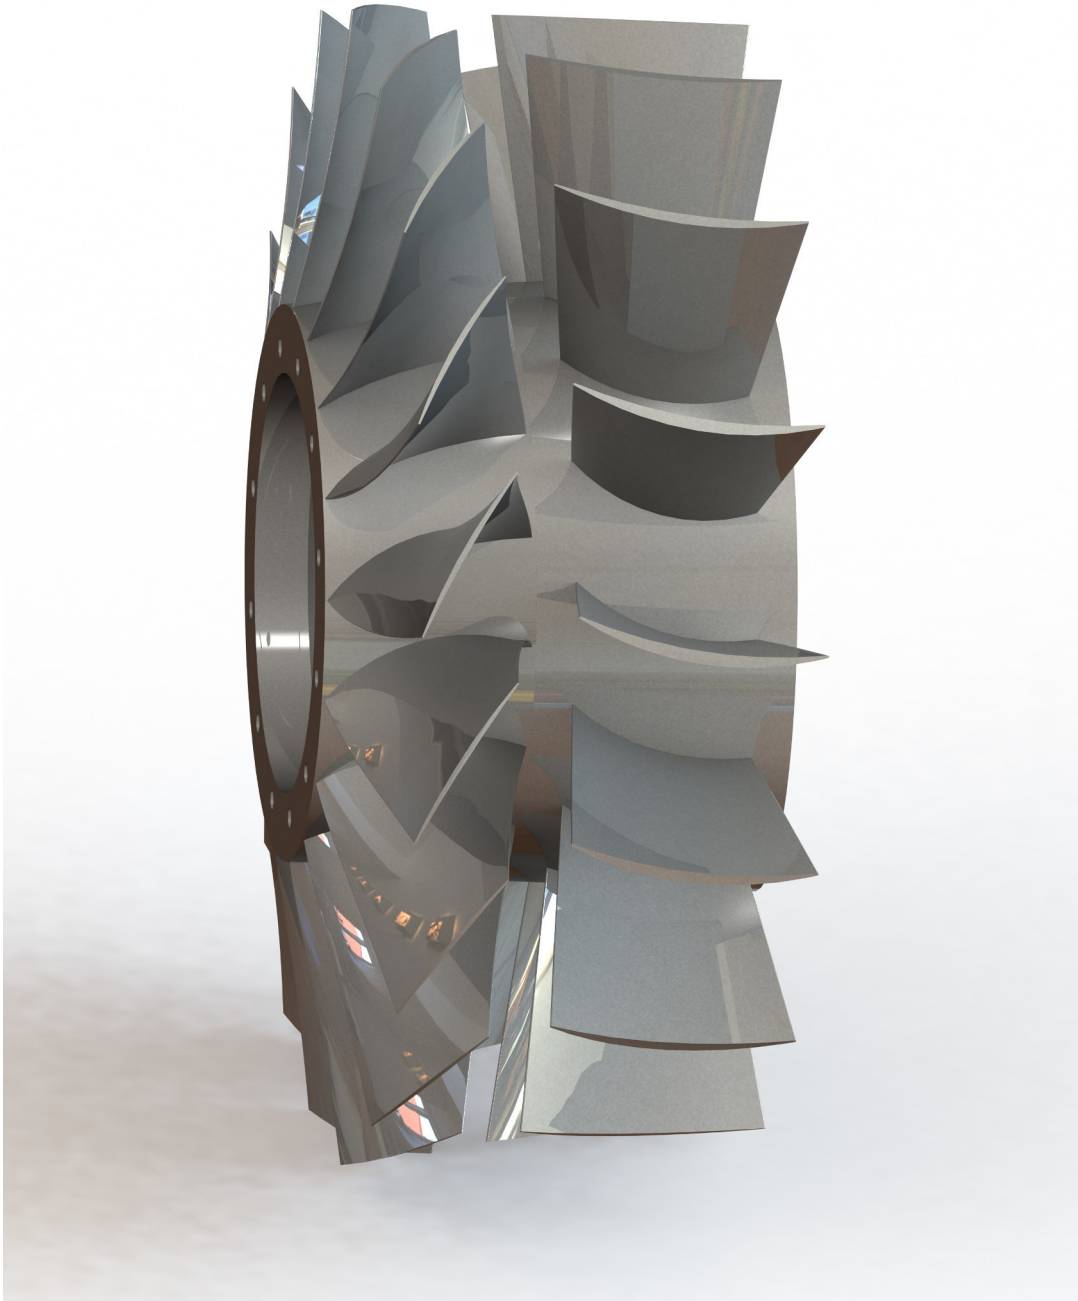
Modelo 3D de la primera etapa del compresor axial. Fuente: Propia.
